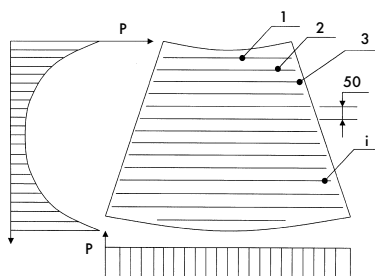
Направление и эпюры изменения усилий при поперечной прокатке листовой детали обшивки диффузора нагнетателя
